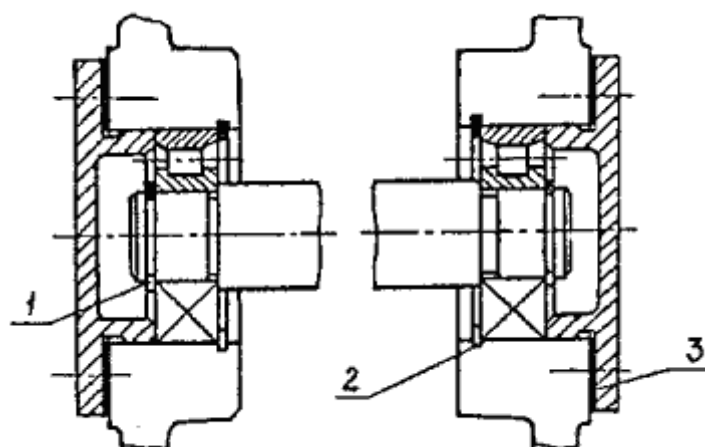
Установка вала на двух плавающих опорах. 2 — плоское пружинное кольцо; 3 — набор прокладок.
